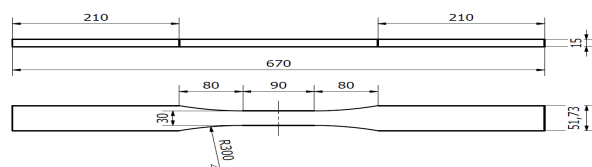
Esquema de la geometría de las probetas con el corte recto (cotas en mm).
